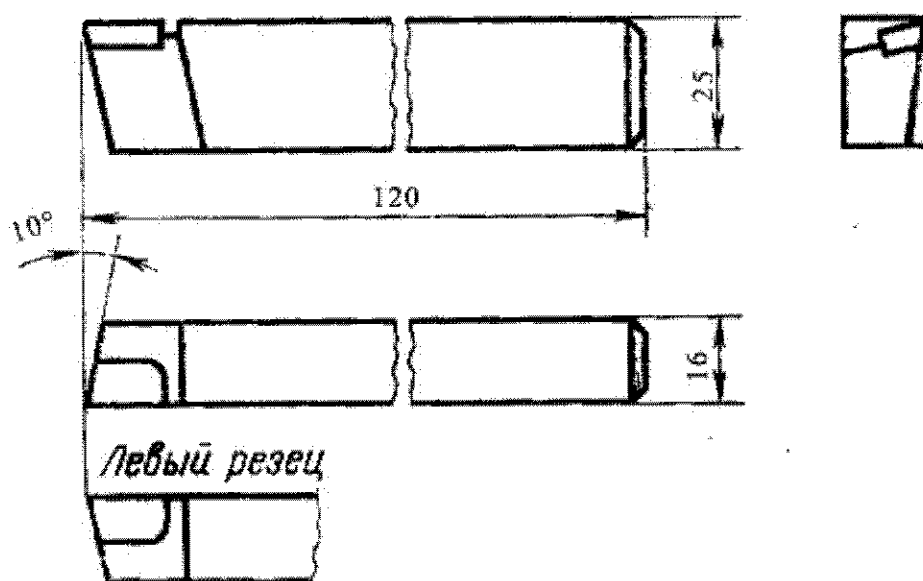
Резец 2101-0014 Т5К10 ГОСТ 18879-73
